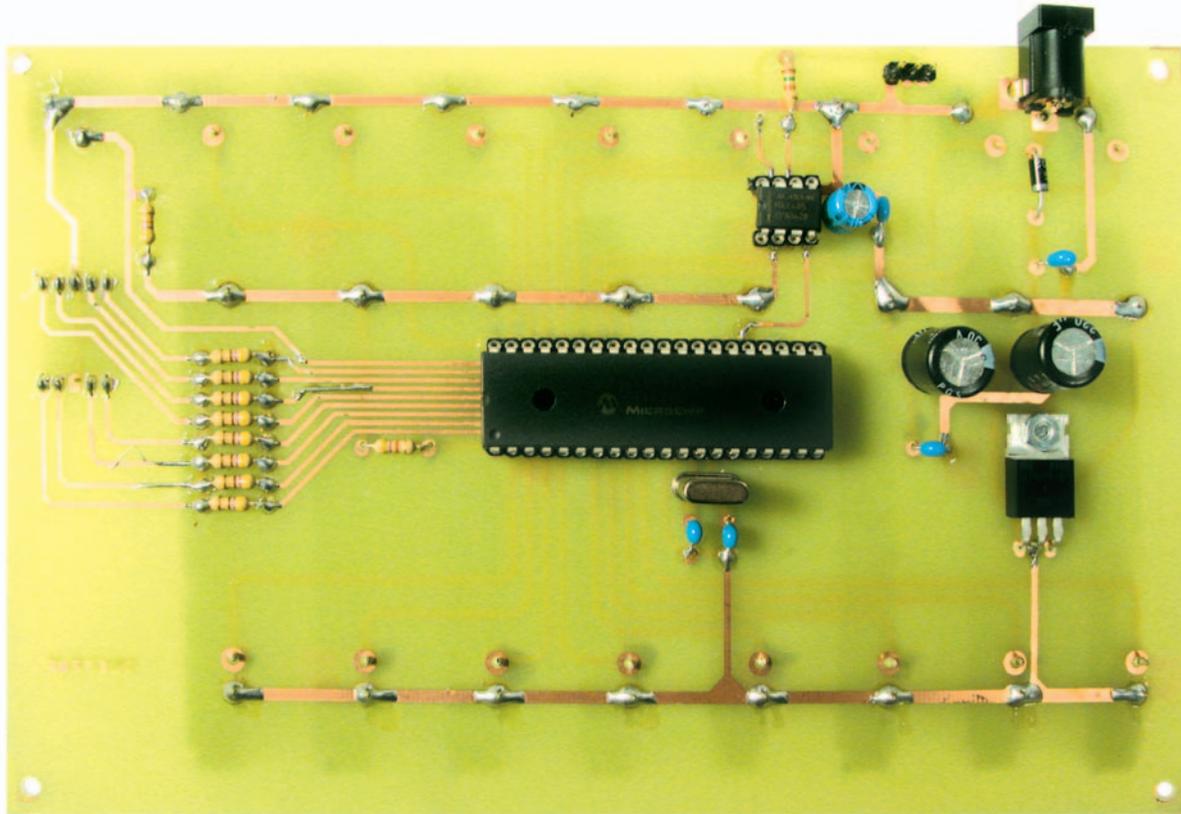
Photo d'un des prototypes de la platine du mélangeur DMX pour régie lumière, côté composants.
